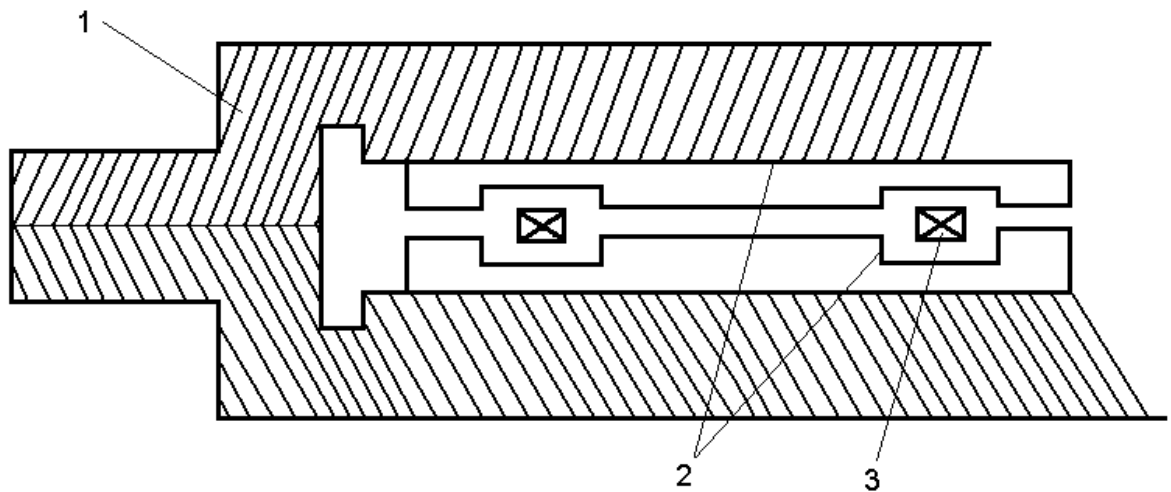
Електромагнітний випромінювач; 1 - корпус; 2 - випромінюючі пластини; 3 - ферромагнітний якір.
